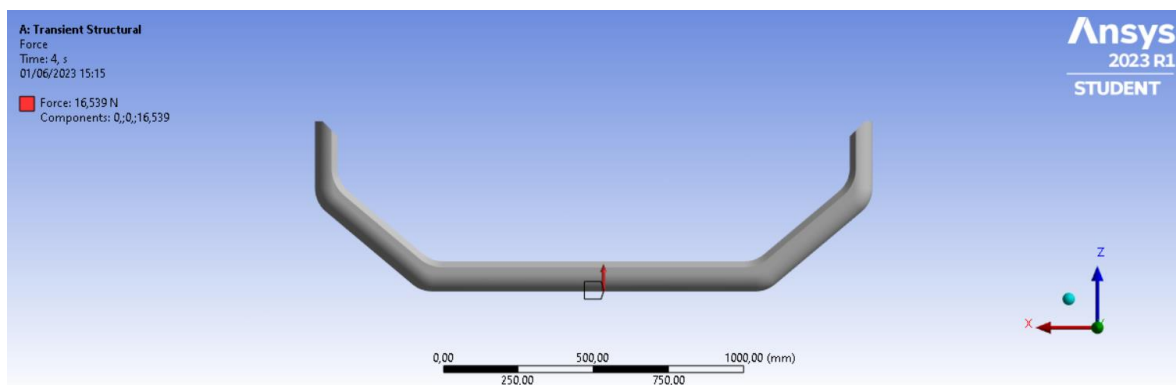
Planta del prototipo del parachoques con la dirección de la fuerza frontal
